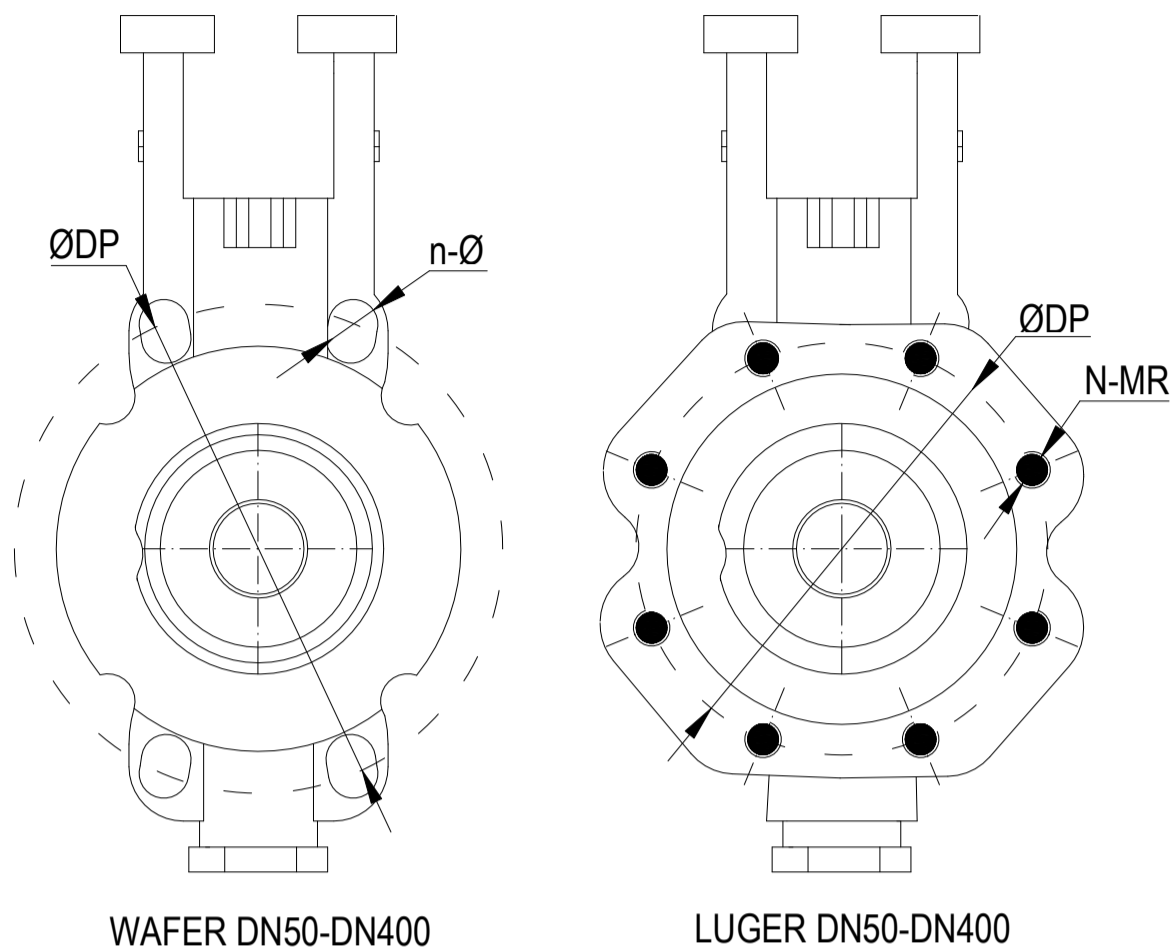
Główne wymiary urządzenia | Main device dimensions | Основные размеры устройства
